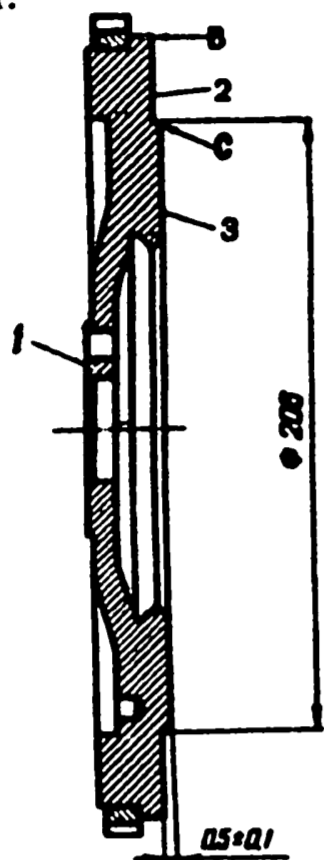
Маховик: 1 - поверхность крепления к фланцу коленчатого вала; 2 - поверхность крепления сцепления; 3 - опорная поверхность ведомого диска сцепления; В - место проверки биения поверхности 2; С - место проверки биения поверхности 3
